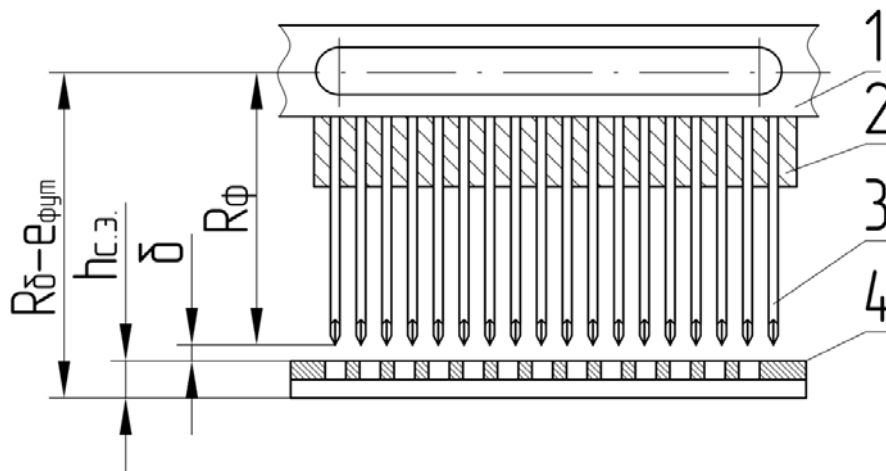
Схема для определения геометрических параметров рабочей камеры агрегата с дисковыми фрезами: 1 – вал; 2 – втулки; 3 – дисковые фрезы; 4 – съемные элементы бандажа
